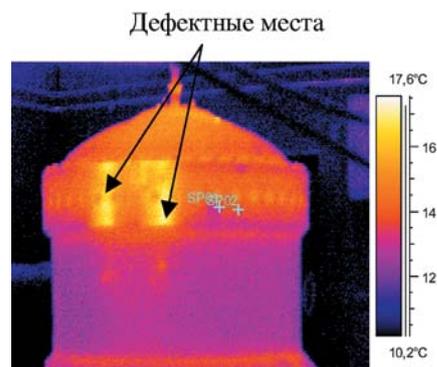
Дефектные зоны на фланцевом соединении баллона под давлением, изготовленного из полимерного материала
